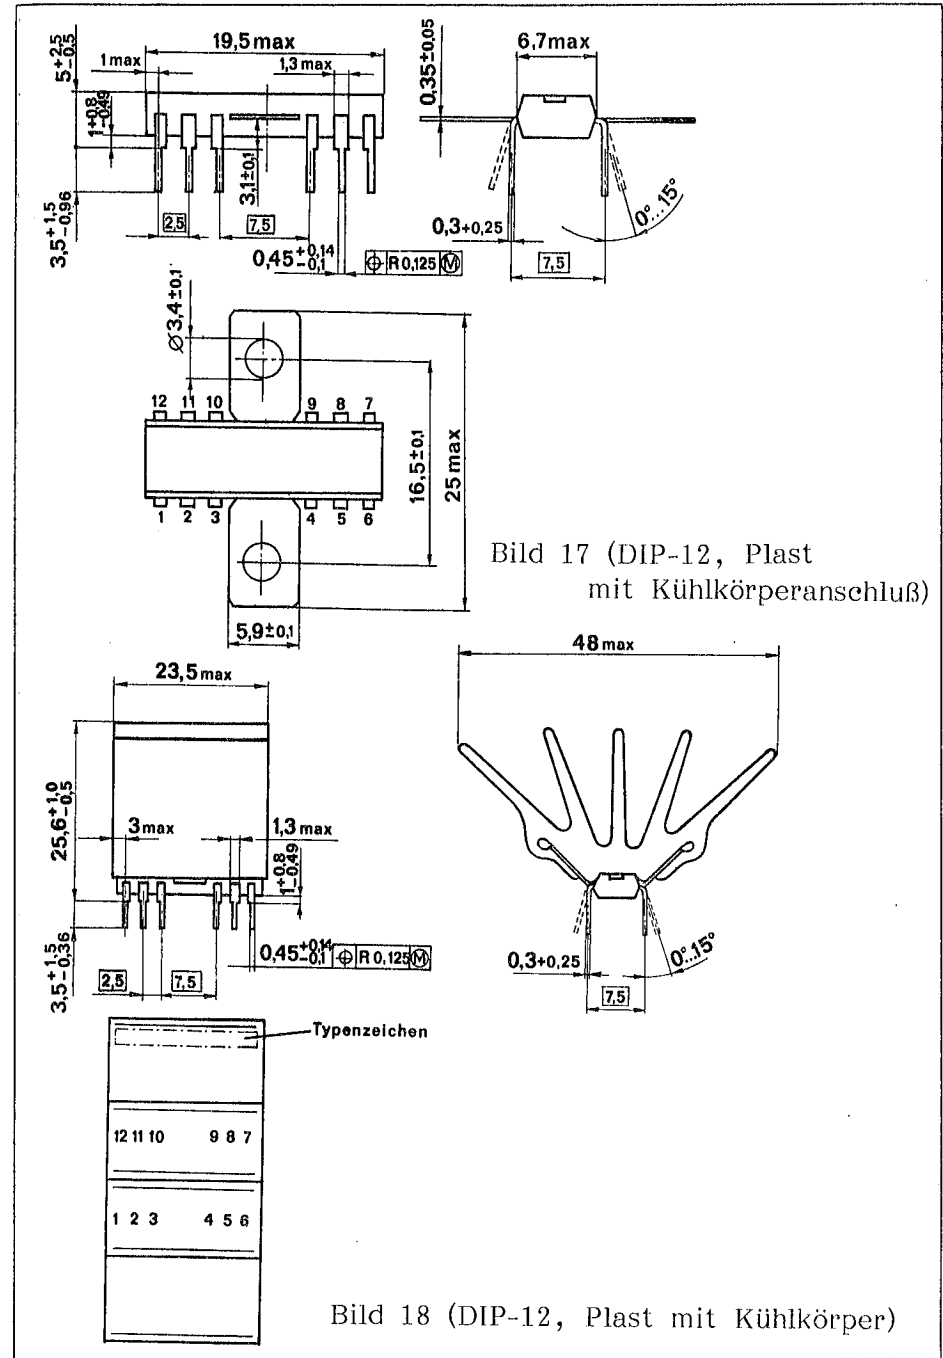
(DIP-12, Plast mit Kühlkörperanschluss)
